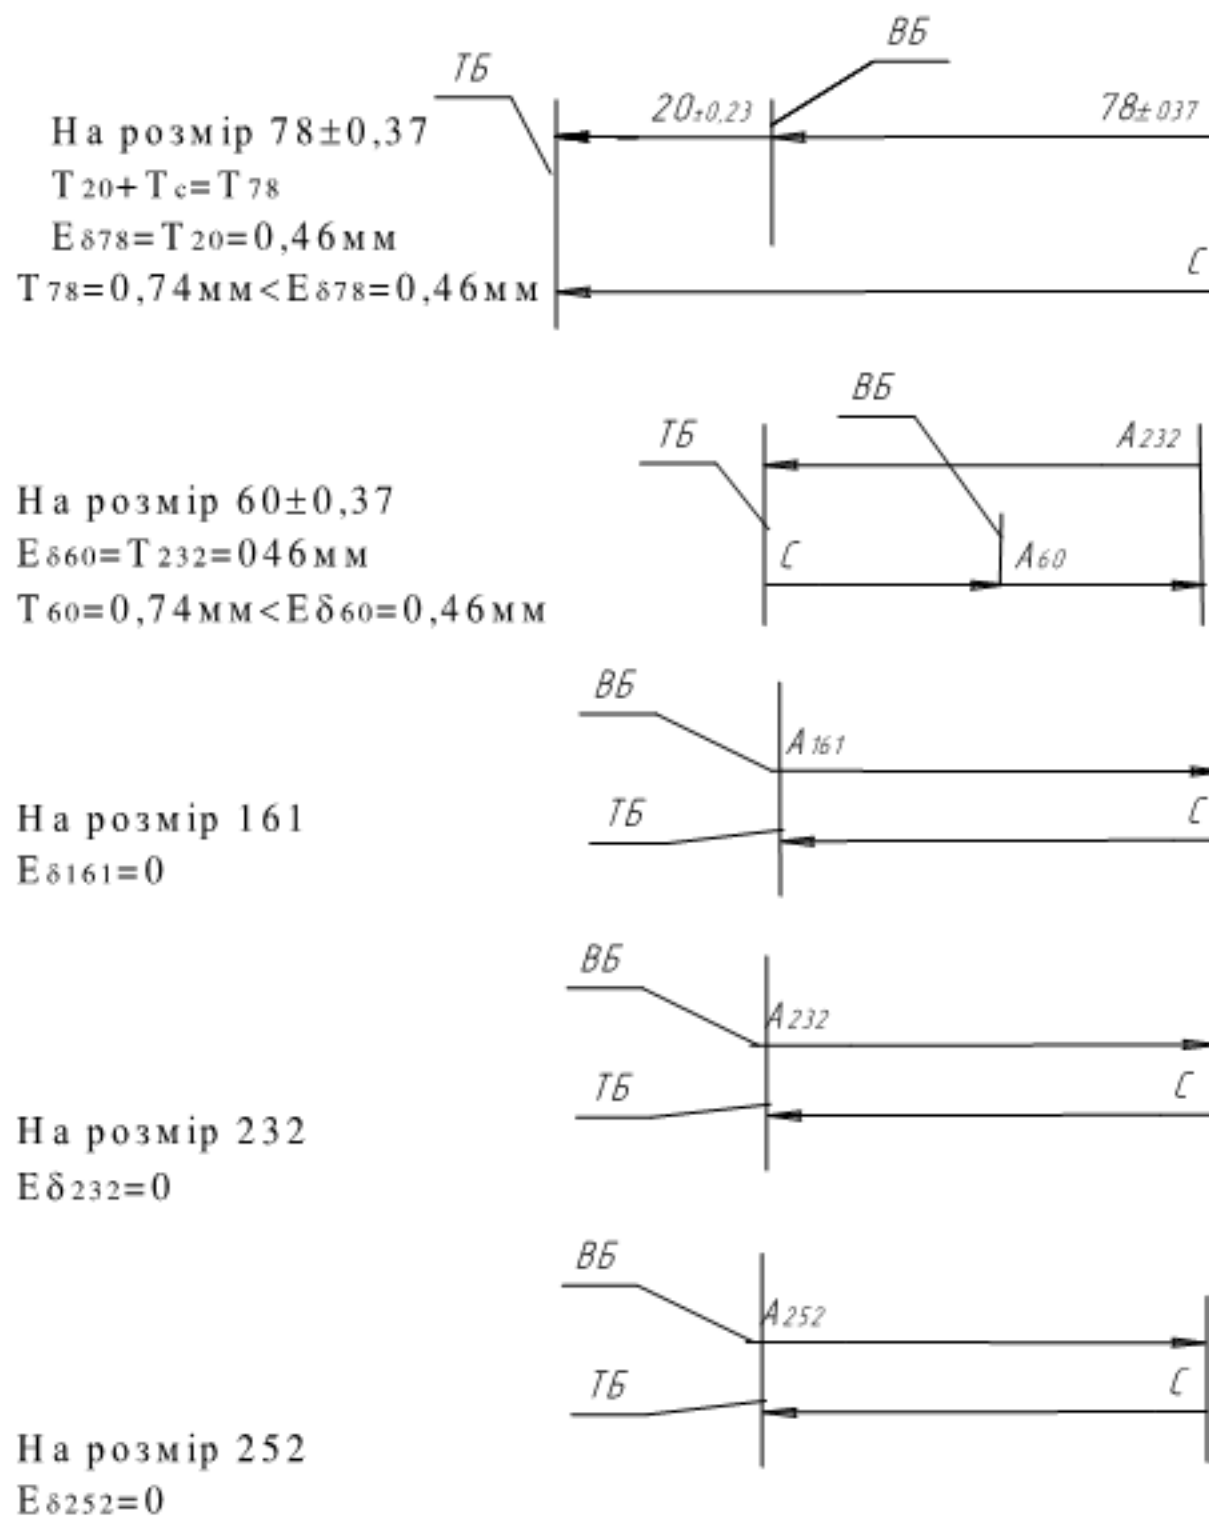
Схема базування заготовки по 1-му варіанту
